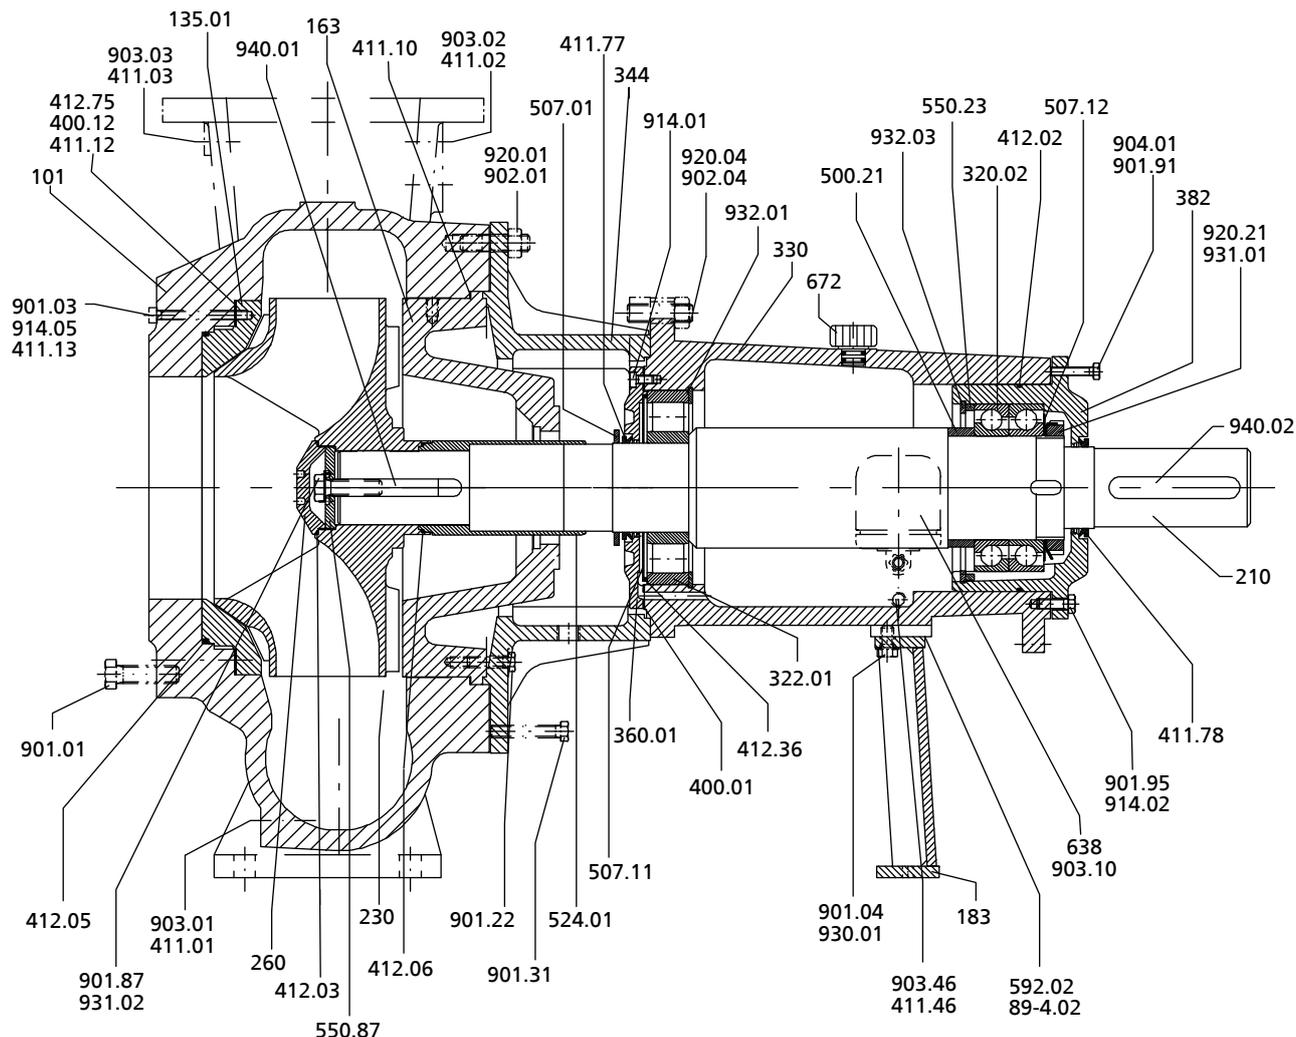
Сборочный чертеж насоса с подшипниковым кронштейном с P08sx по P12sx
